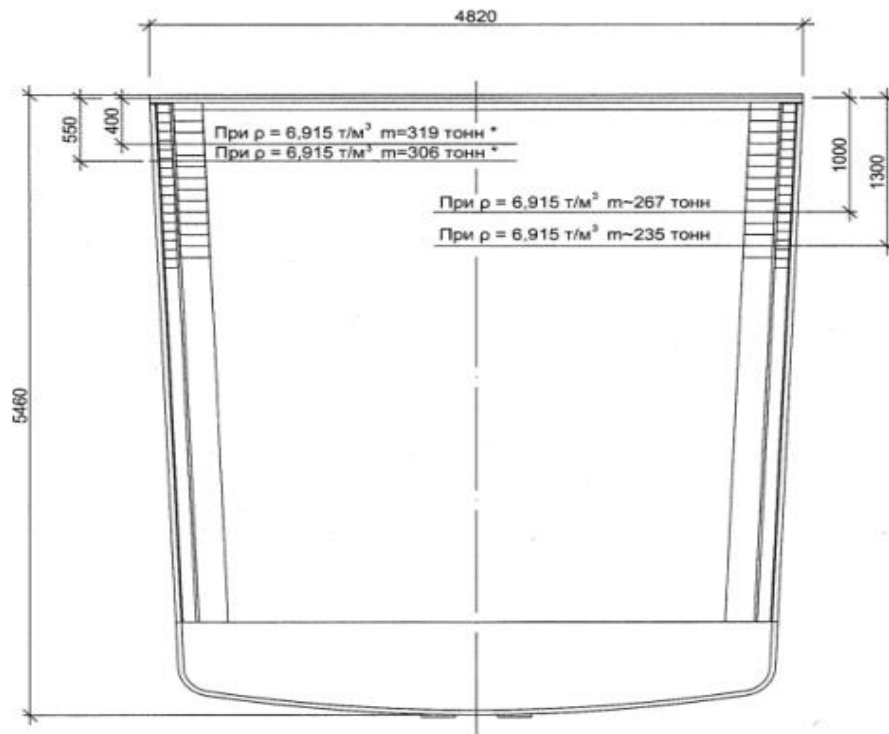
Масса металла в сталеразливочном ковше при вакуумировании
